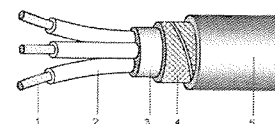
Struttura di un cavo tripolare con armatura metallica
